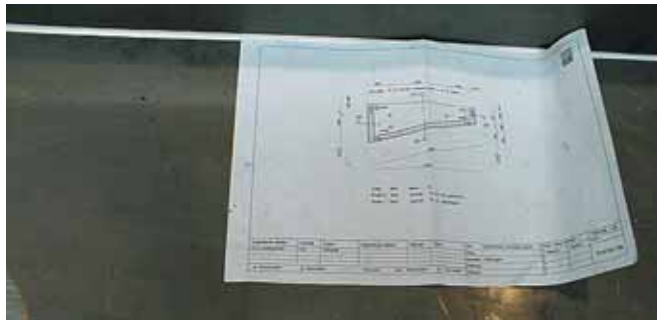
Mal voor plaat met verdieping, driehoekige vorm
